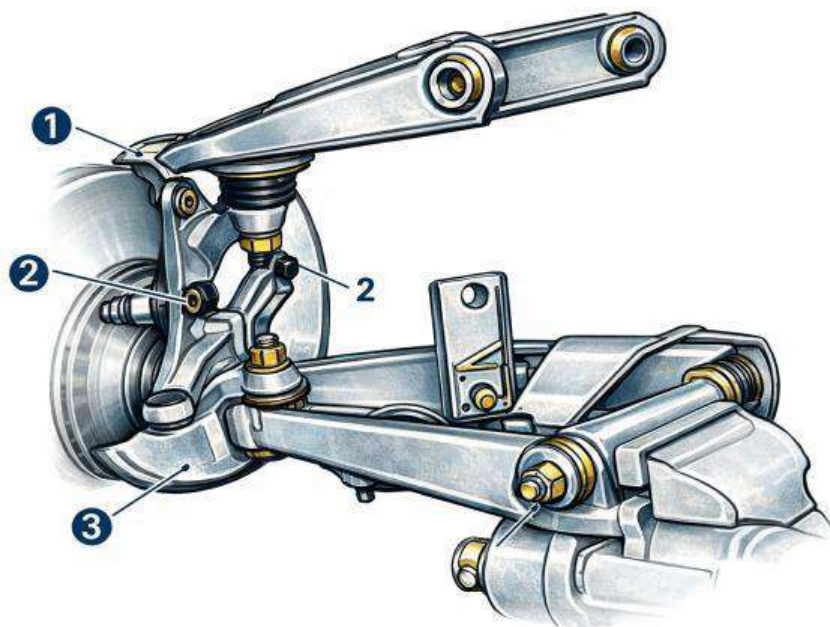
Вузол підвіски лівого колеса, закріпленого на верстаті для розбирання: 1 - гайки кріплення важіля обертового кулака, кронштейна кріплення супорта і захисного кожуха до обертового кулака; 2 - кронштейн кріплення супорта; 3 - захисний кожух гальмівного диска
